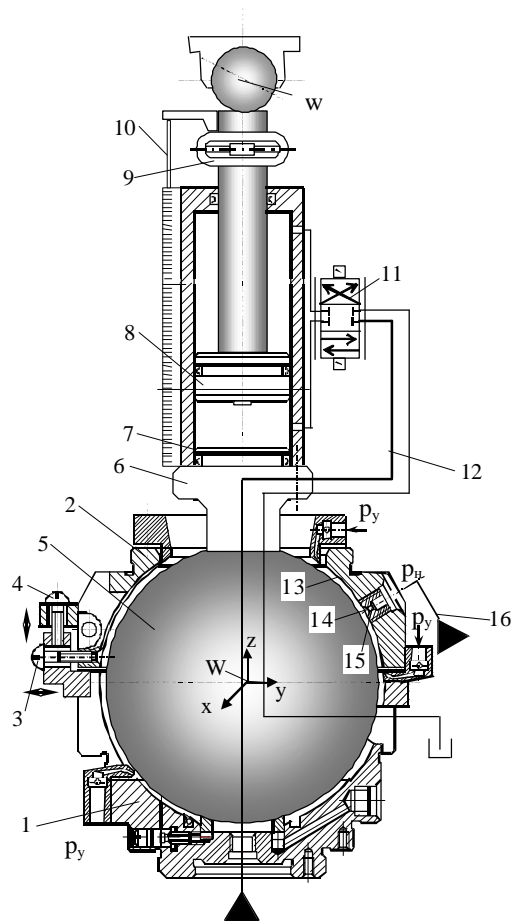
Конструктивна схема сферичного шарніра рідинного тертя та з'єднаної з ним штанги з приводом зміни її довжини
